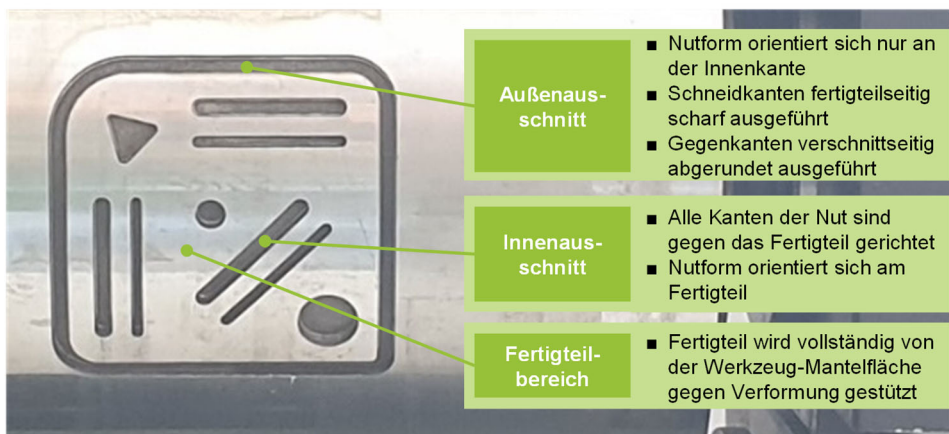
Werkzeugkavität zum rotativen Elastomer-Schneiden
